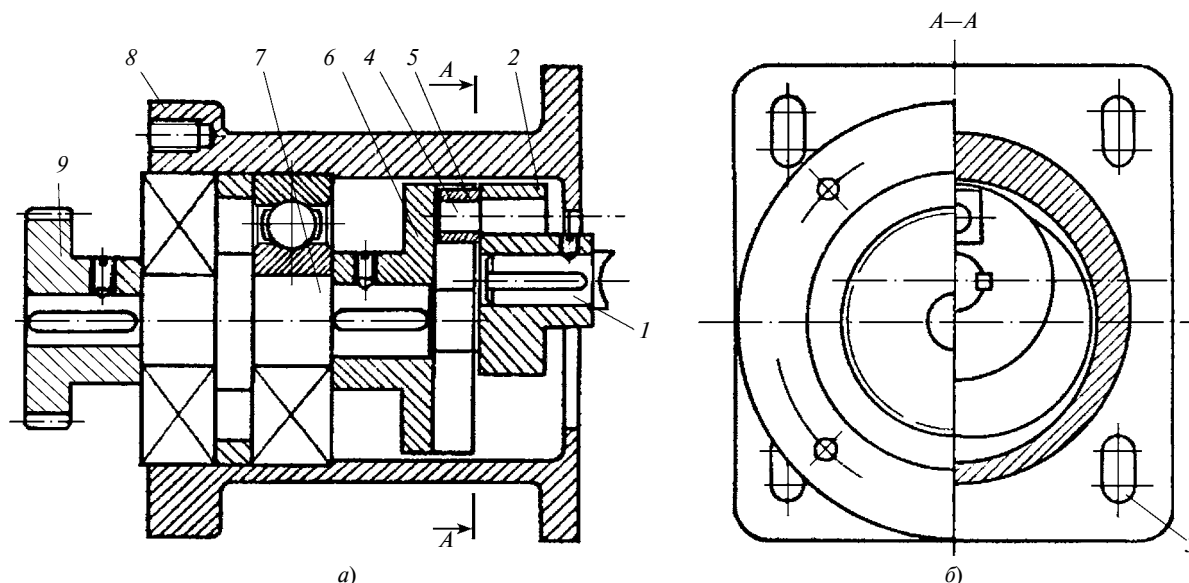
Конструкция вибропривода для генерации крутильных колебаний шпинделя головки глубокого сверления
